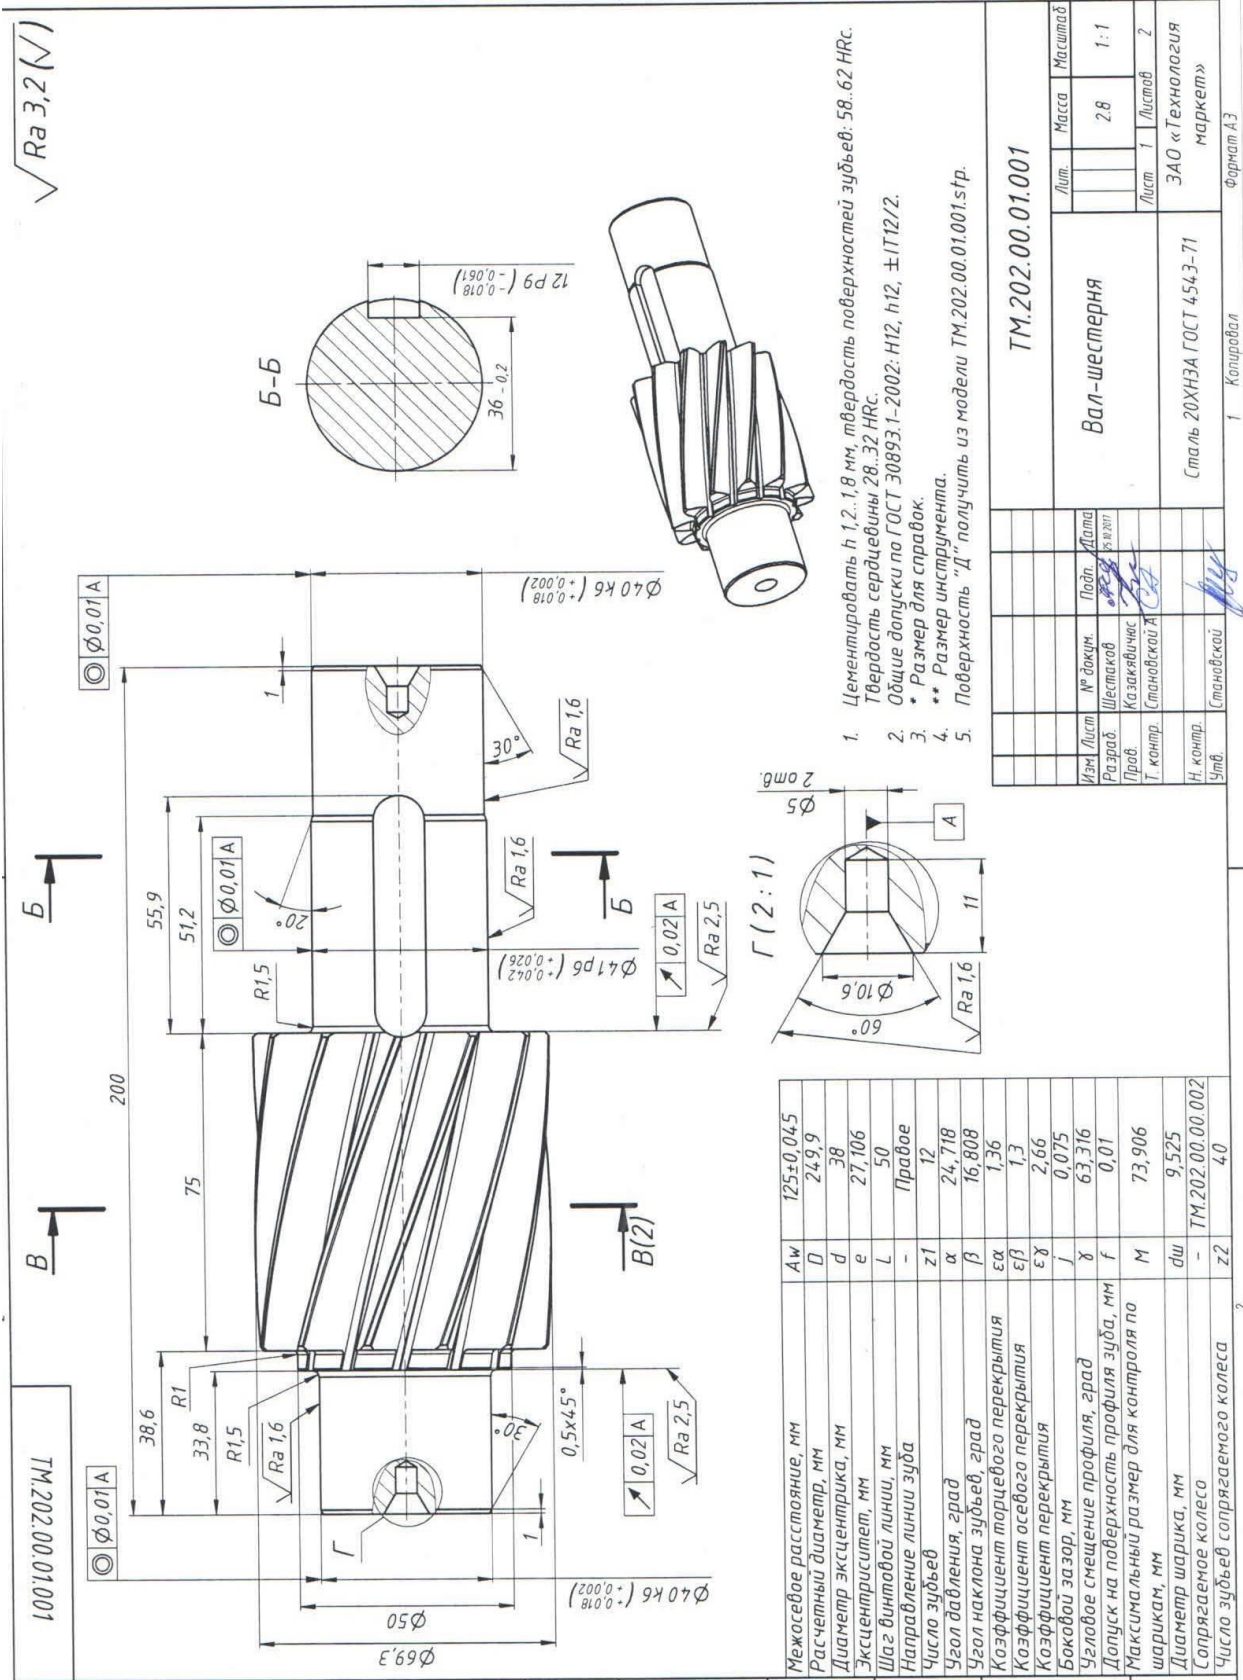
Чертеж вала-шестерни редуктора с ЭЦ зубчатым зацеплением
